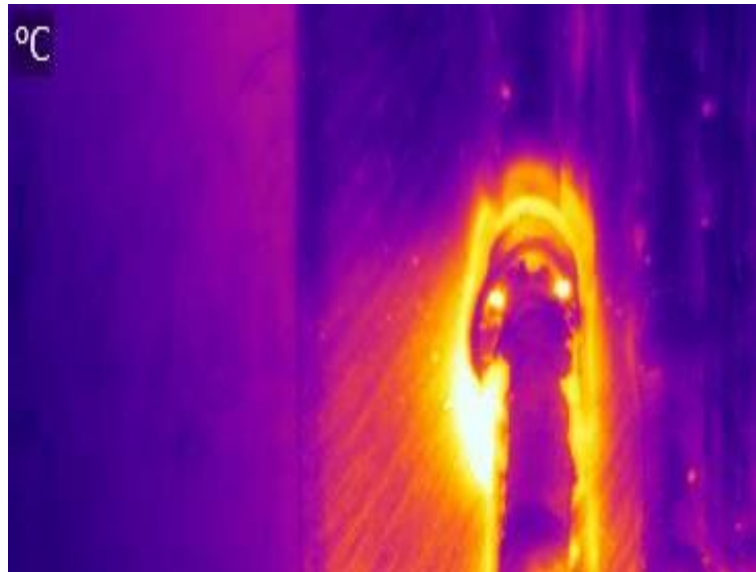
Cordón de soldadura afectado por porosidad (2).
